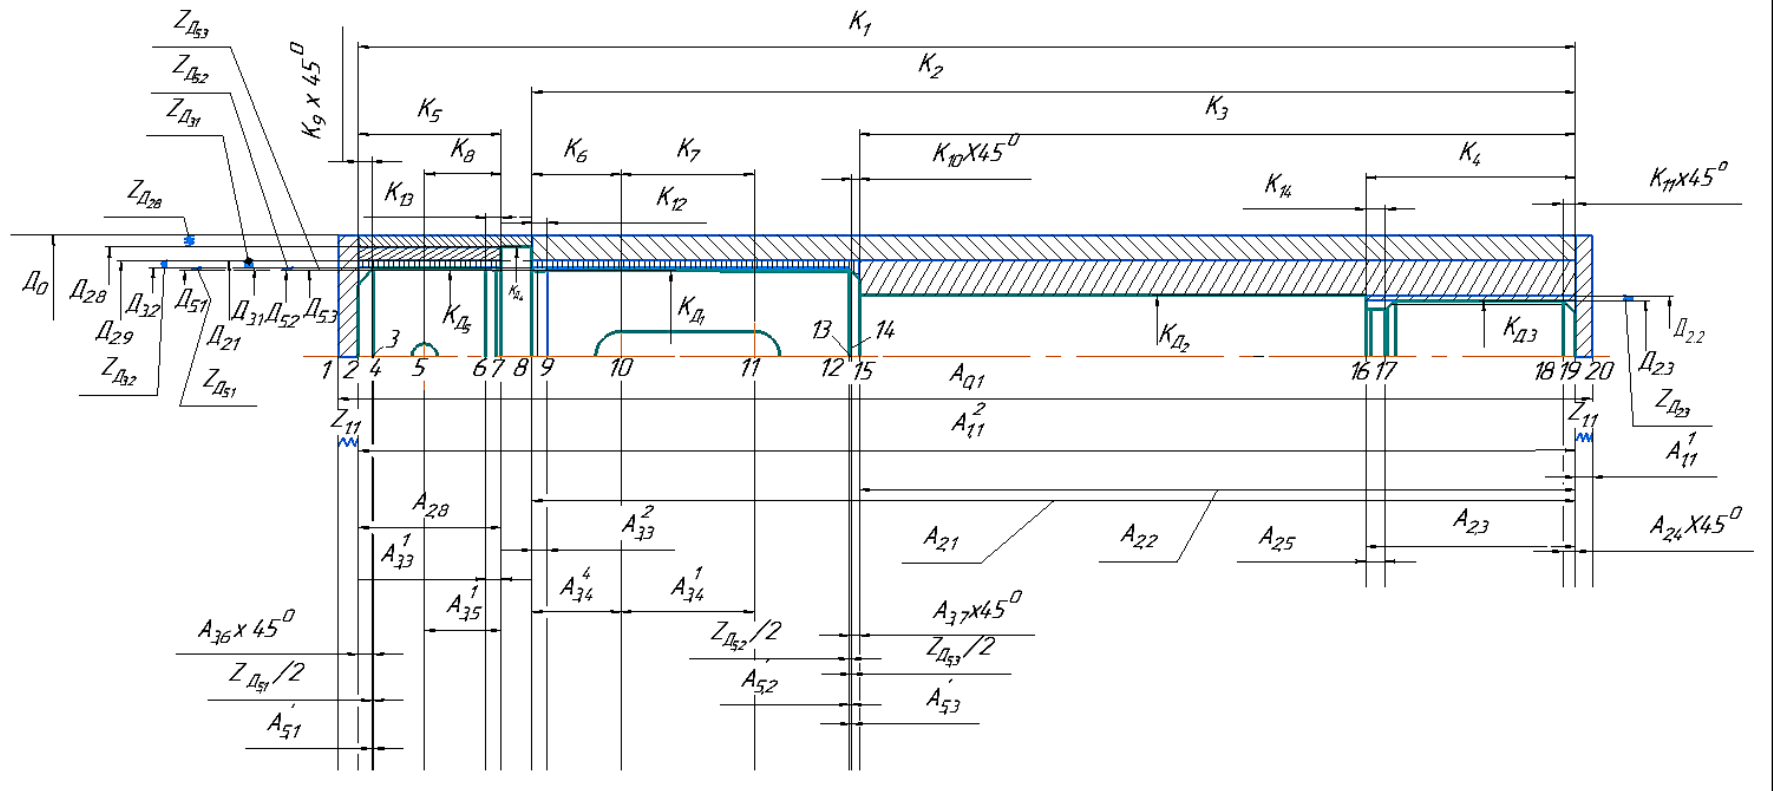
а - Размерная схема технологического процесса изготовления стержня
